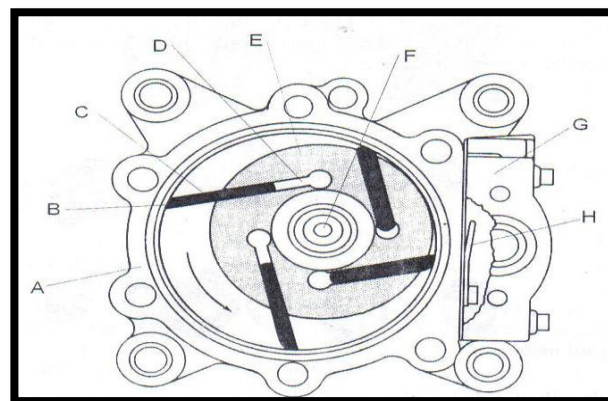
PARTES DEL COMPRESOR ROTATIVO DE PALETAS
